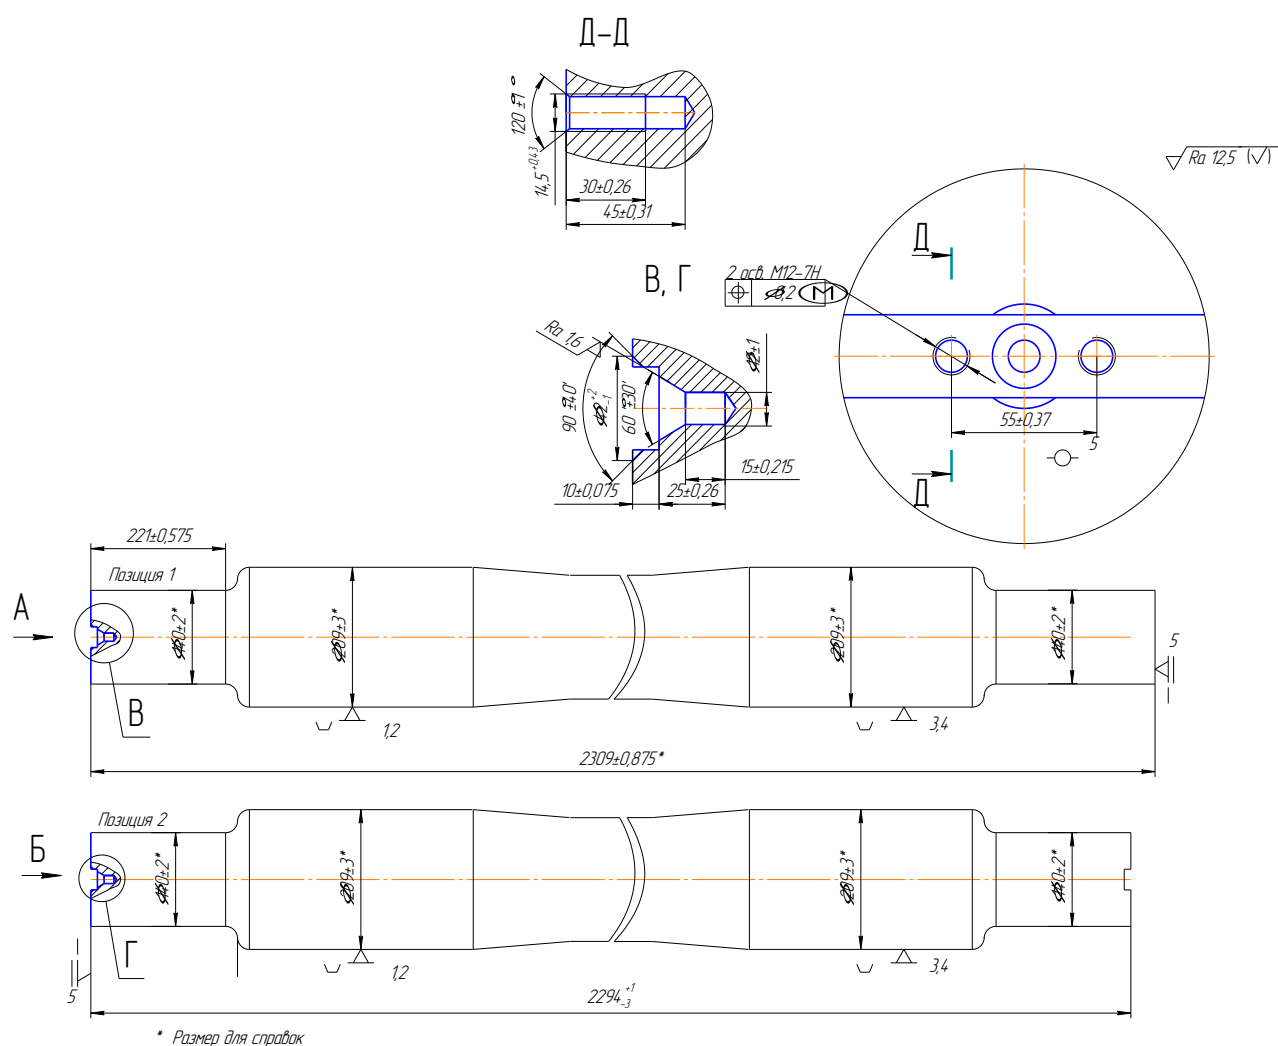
Схема базування «Осі» з упором в торець
